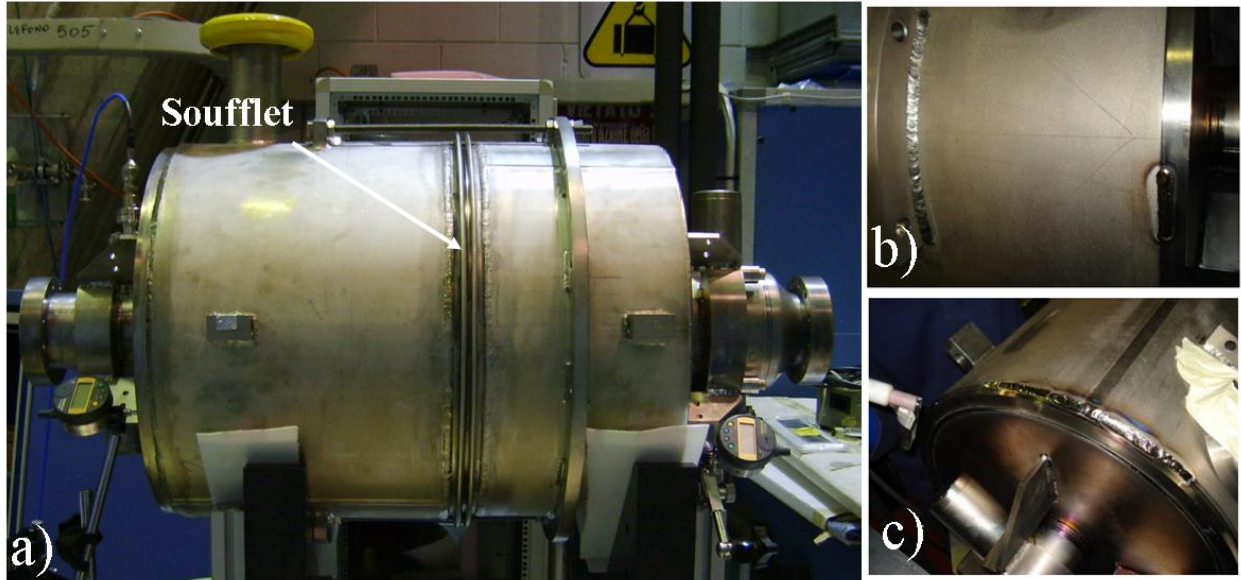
a) La cavité Psyché équipée de son tank hélium composé de deux parties reliées par un soufflet. b) et c) Détails de la procédure de soudage du tank en titane.
